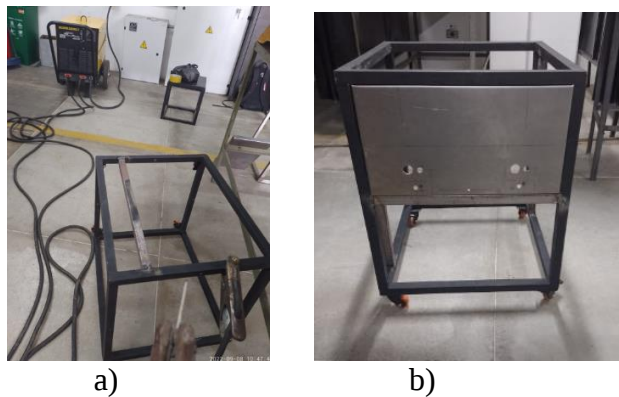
a) y b) Construcción de la estructura para montar los equipos.
